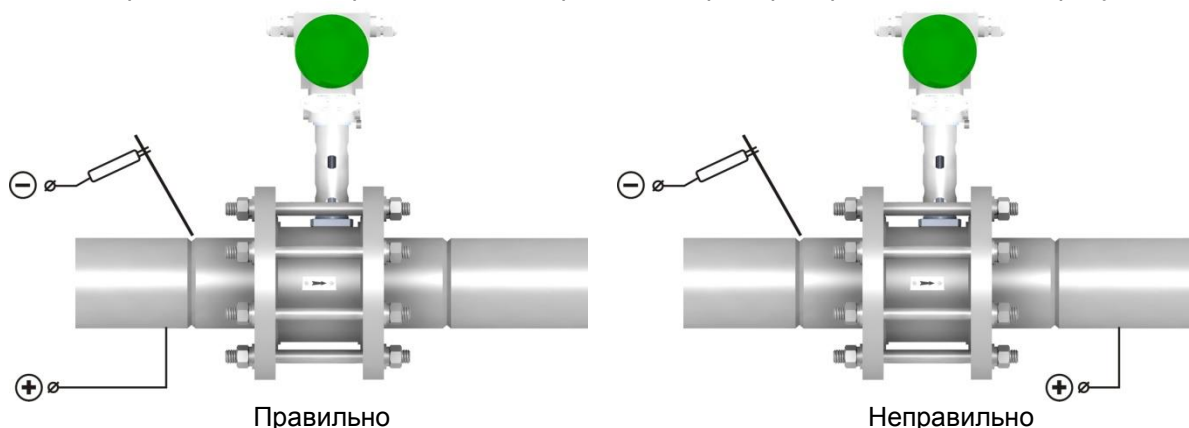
Подключение источника тока при электродуговой сварке
